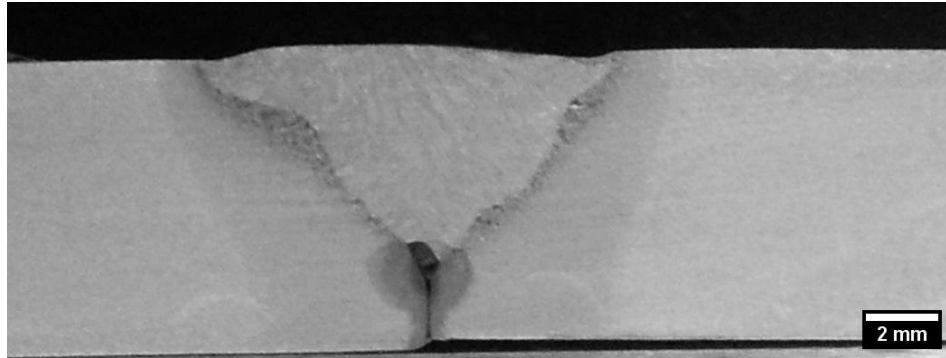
Condição (B). Soldagem convencional com pré-aquecimento à 100°C e pós-aquecimento à 230°C por uma hora.
